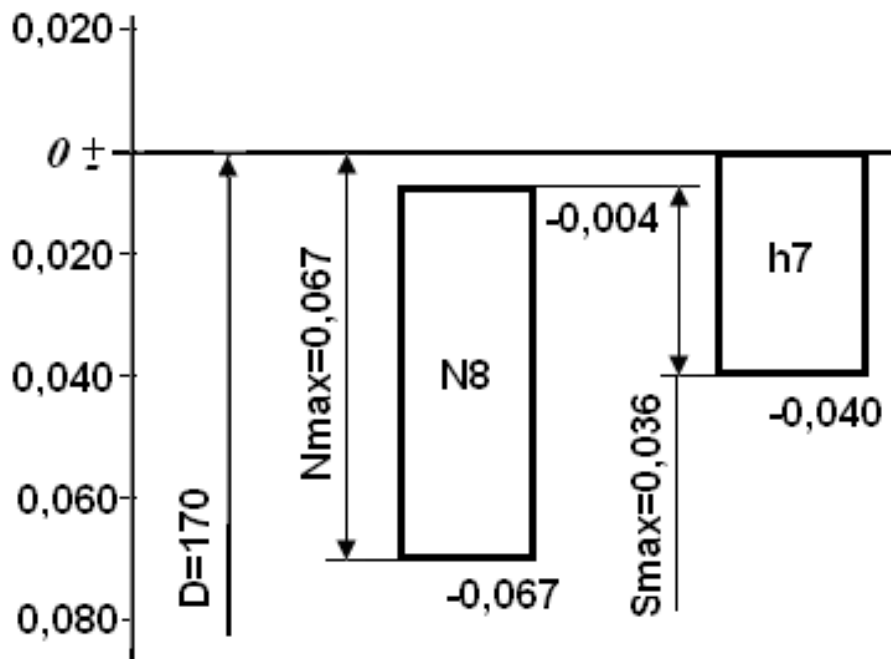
Схема розташування полів допусків деталей з'єднання  $\varnothing 170N8/h7$
